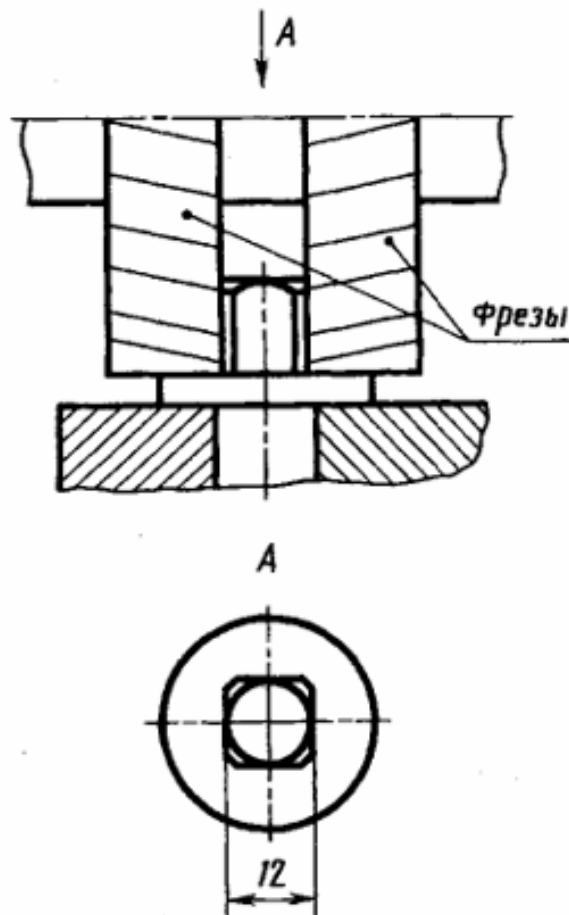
Пример фрезеровки головки ступенчатого валика двумя фрезами
